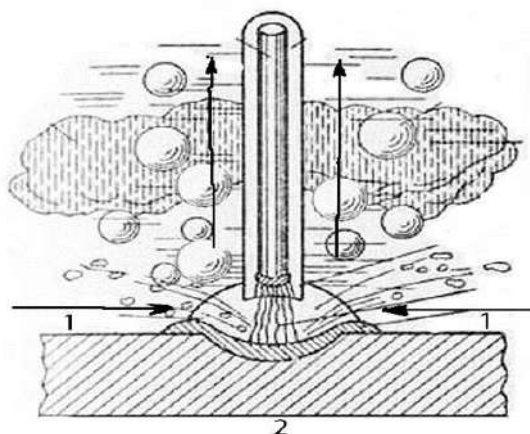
Подводная сварка покрытыми электродами в нижнем положении. 1 - верхняя поверхность пластины. 2 - нижняя поверхность пластины.
